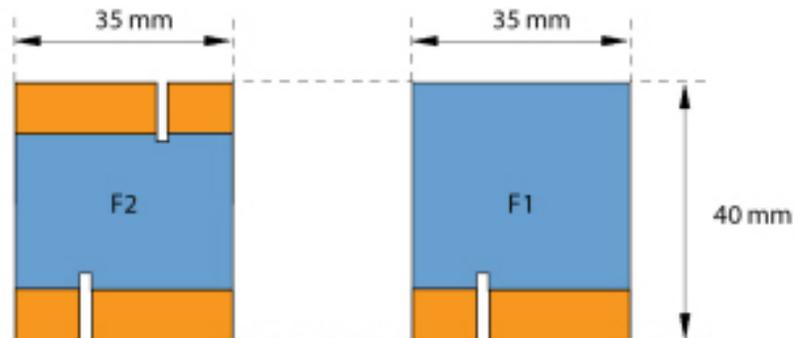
Dimensiones del adaptador de cableado (dibujo F)
